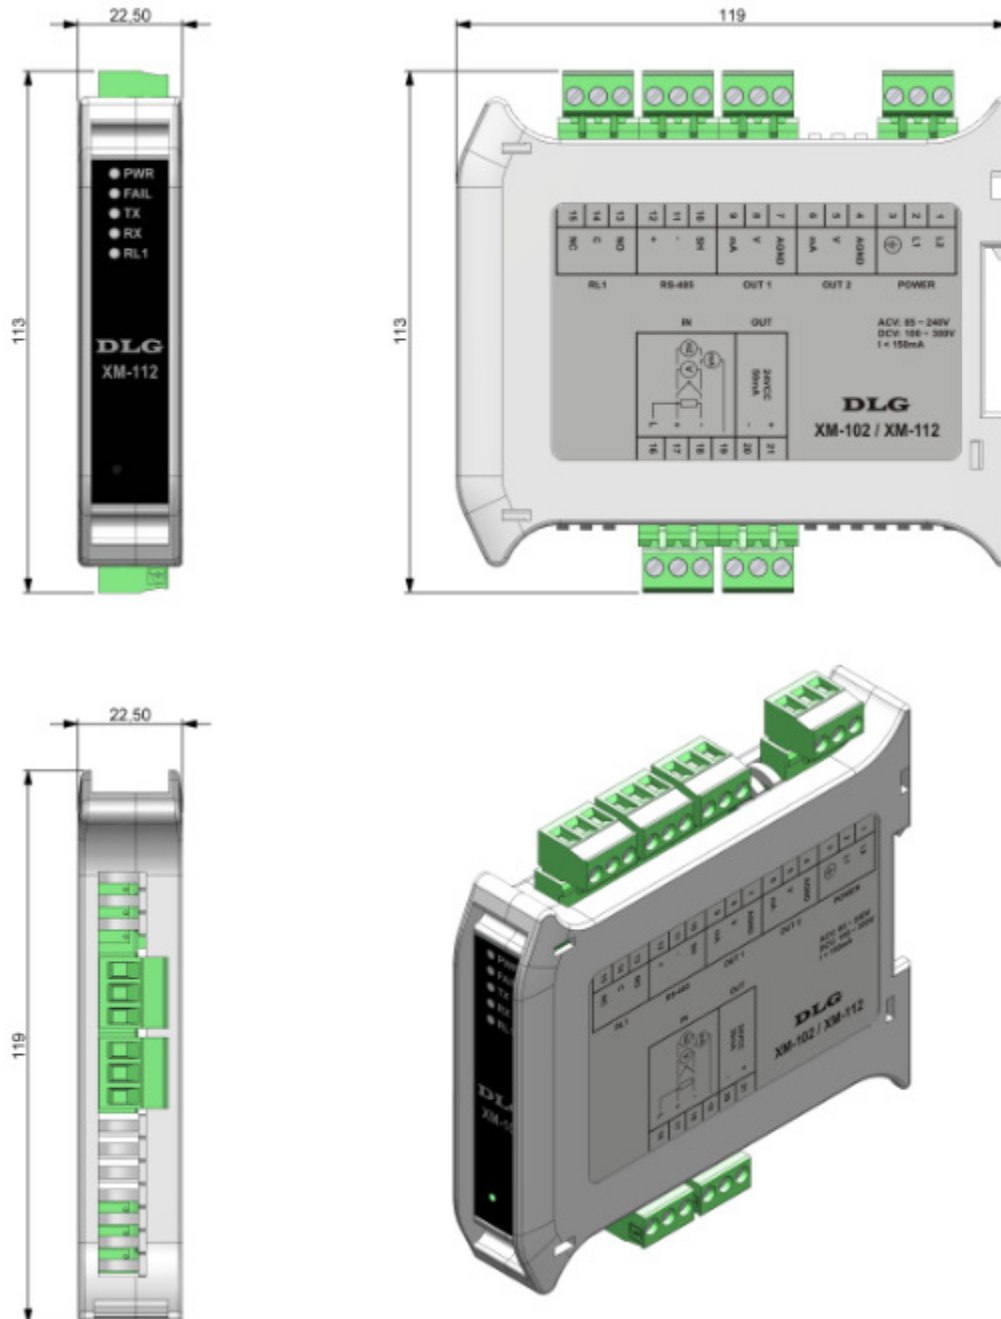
Dimensionamento para montagem (Cotas em milímetros)
